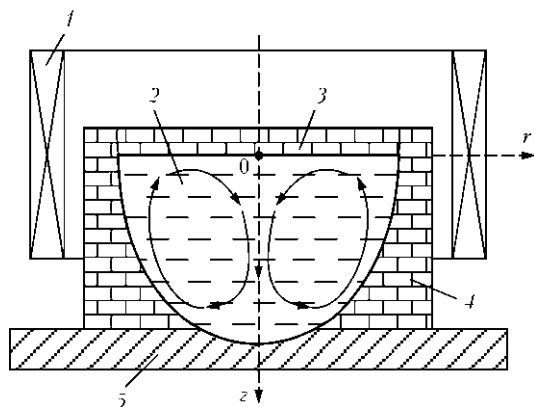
Схема движения потоков расплавленного металла в тигле при обработке изделий предложенным способом: 1 — индуктор; 2 — расплавленный металл; 3 — крышка тигля; 4 — тигель; 5 — изделие
